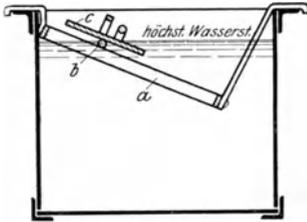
Vorrichtung zum Härten kleiner Spiralbohrer. (Aus Brearley-Schäfer, Werkzeugstähle.)
